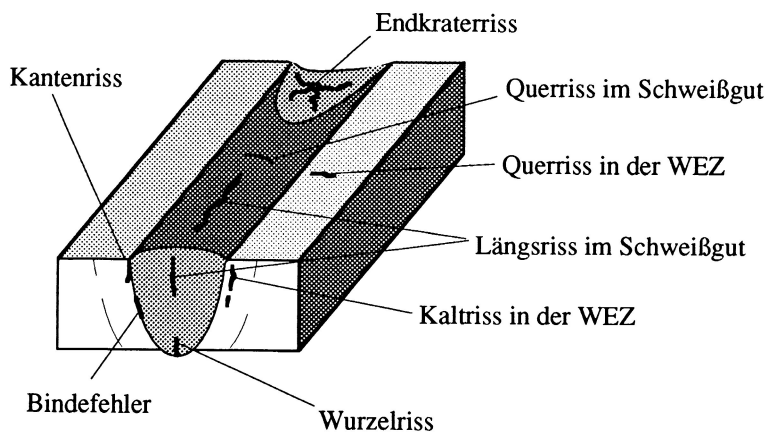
Typische Rißarten in einer Schweißverbindung /102/
